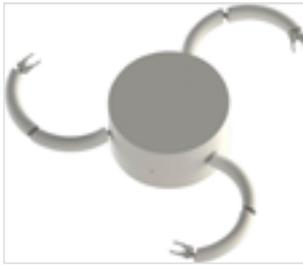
Elaborazione CAD del prototipo dimostratore. Vista esterna
